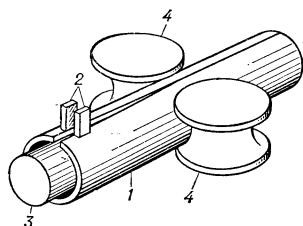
Схема сварки труб контактным способом: 1 — труба; 2 — контактные электроды; 3 — сердечник; 4 — обжимные ролики.
